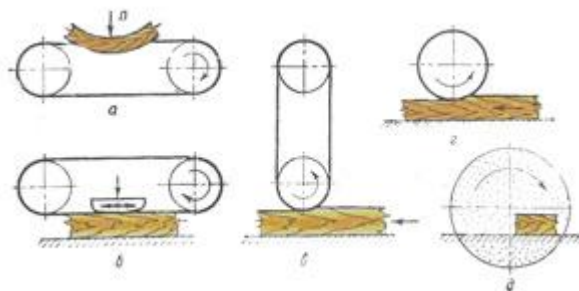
Схемы шлифования на деревообрабатывающих станках: а - со свободной лентой;
